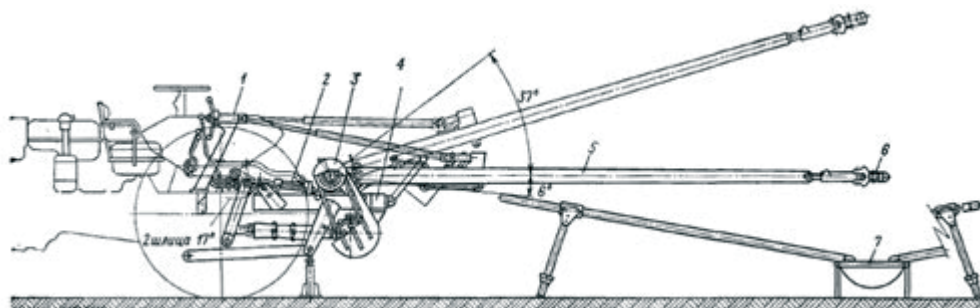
Схема плодуборочной машины ВСО-25 «Стрела» с улавливающим приспособлением УП-5
